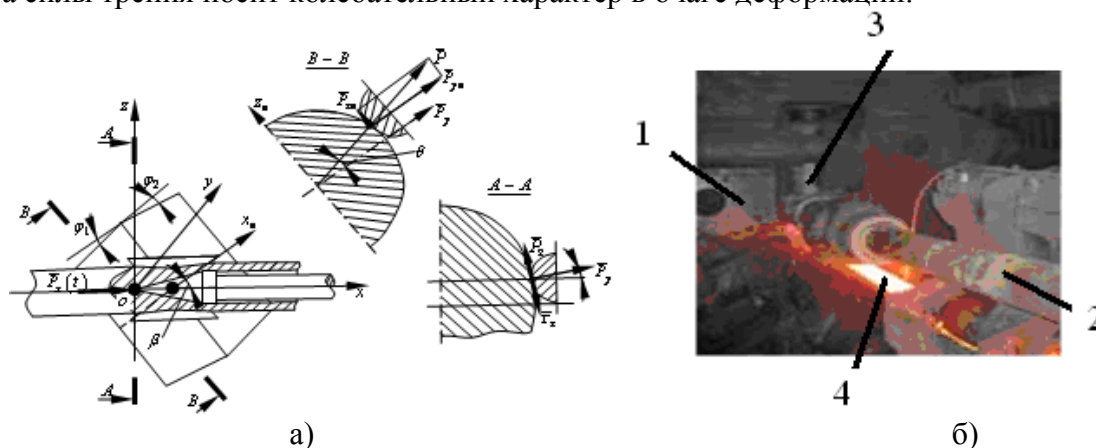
Процесс прошивки трубной заготовки на стане винтовой прокатки труб: а – очаг деформации в процессе прошивки; б – процесс прошивки трубной заготовки
